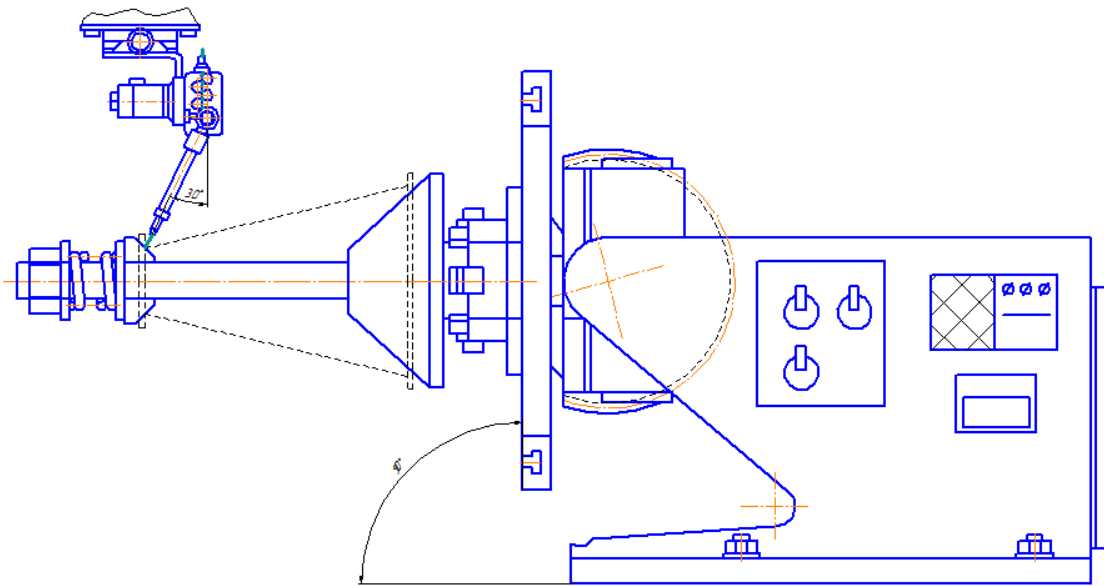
Схема налаштування обладнання для зварювання
